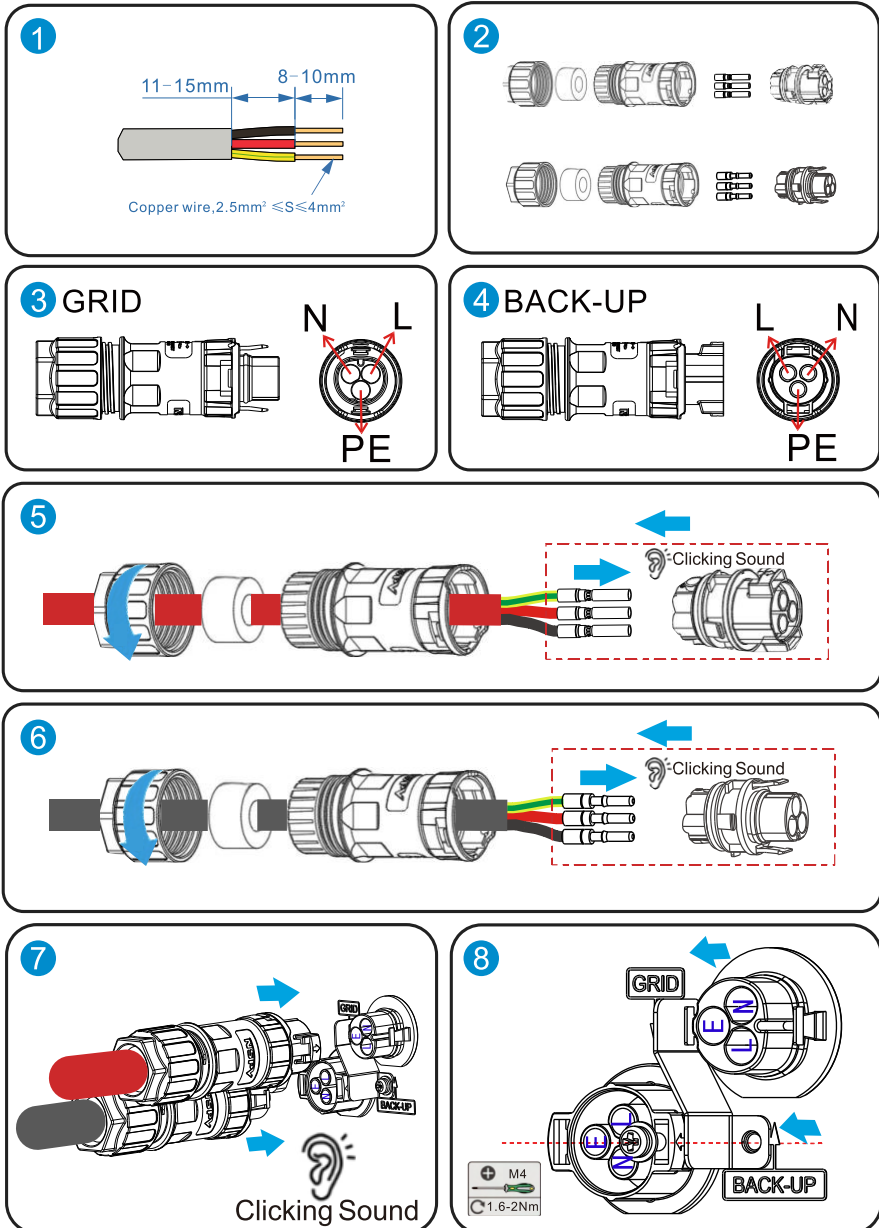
Passaggi per l'installazione e il collegamento del cavo AC
